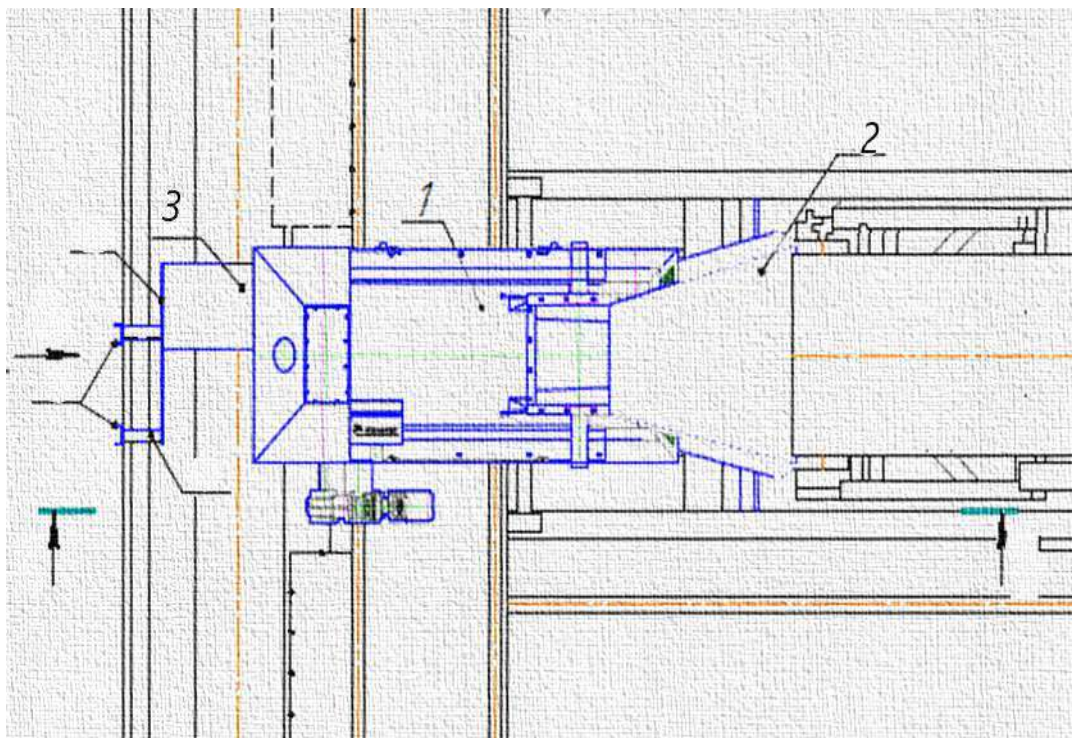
Схема реконструкции узла окомкования (вид сверху):
